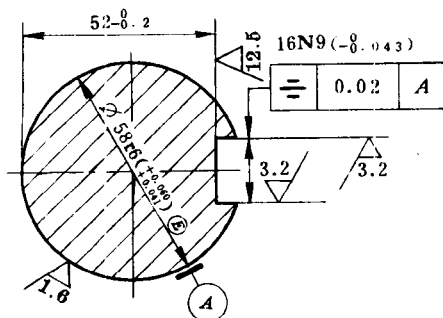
轴键槽尺寸和公差标注示例
